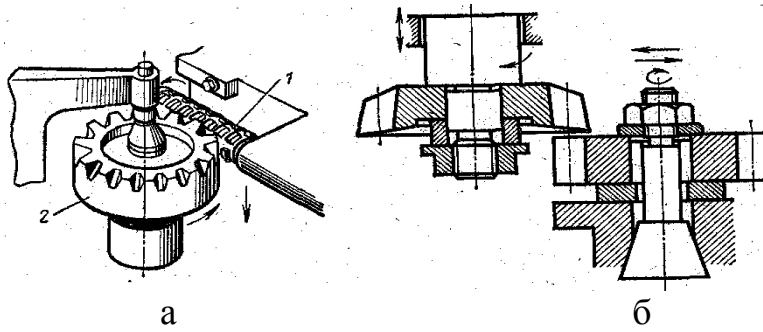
Нарізання зубчатих коліс черв'ячною фрезою та зуборізним довбачем
